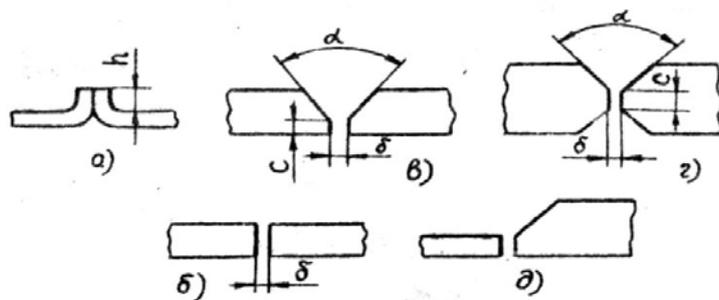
Подготовка (разделка) кромок под стыковой шов
